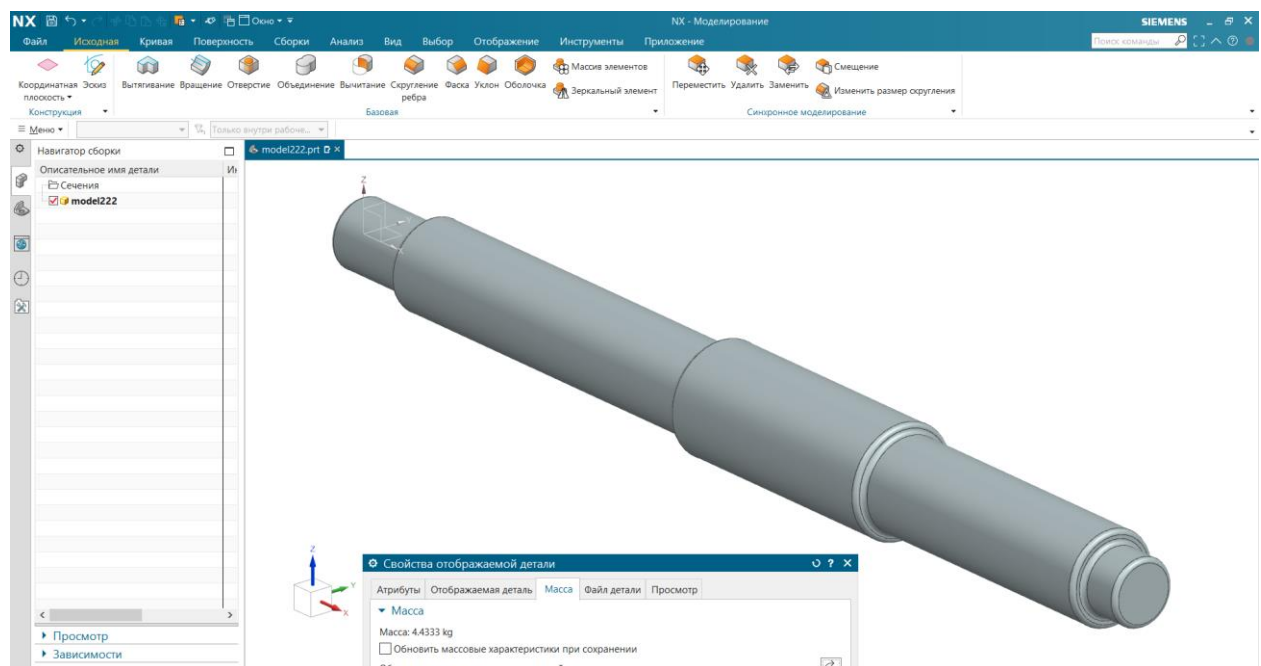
Ескіз заготовки отриманої на КГШП
